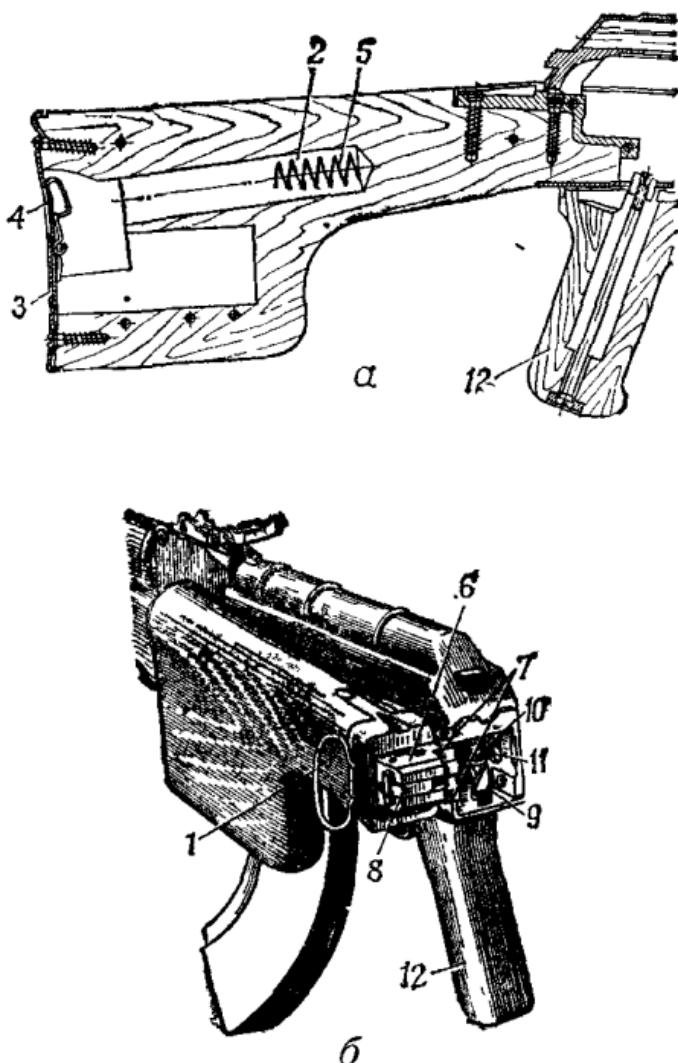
Приклад и пистолетная рукоятка пулемета:
